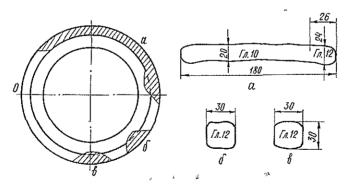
Выборка металла сварного шва штуцера коллектора
